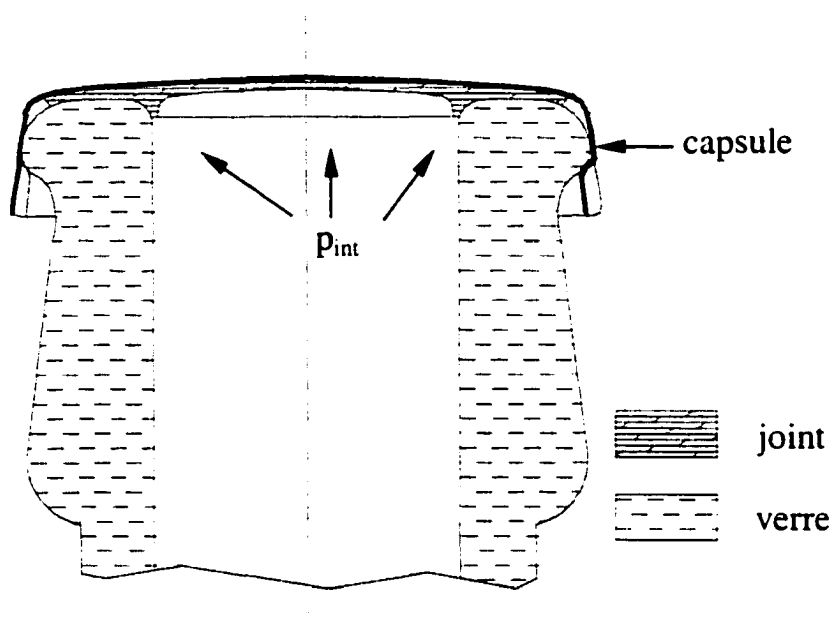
Vue en coupe d'un assemblage capsule-bouteille
